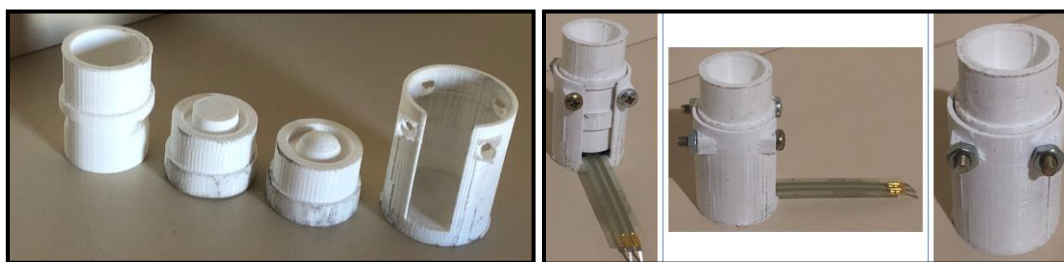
Componentes impressos do dispositivo (esq.) sistema de captura de forças montado (dir.).
